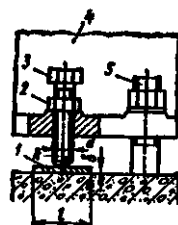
Схема выверки отжимными регулировочными винтами
